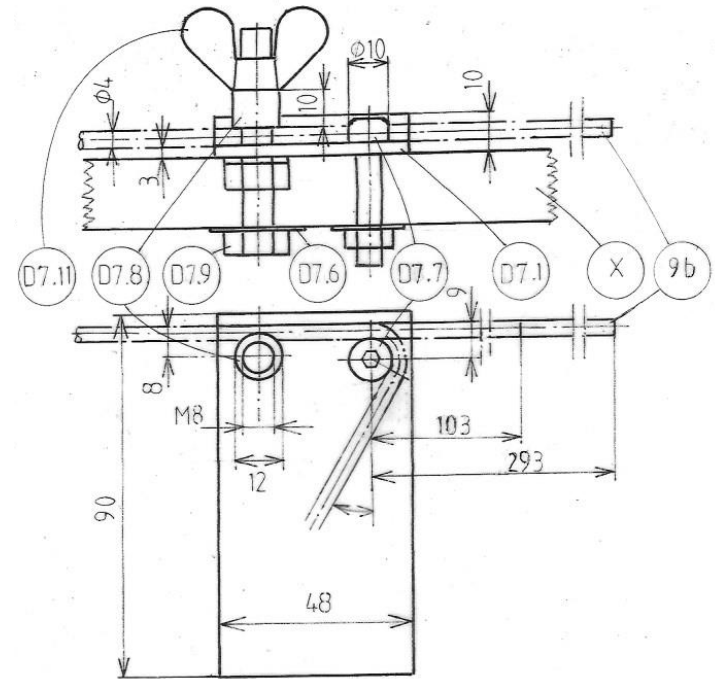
Dibujo del dispositivo D7 para doblar triángulo del recipiente (7), de acero (soporte soldado), o de aluminio o acero inoxidable (soporte con abrazaderas); diámetro: 4 mm
